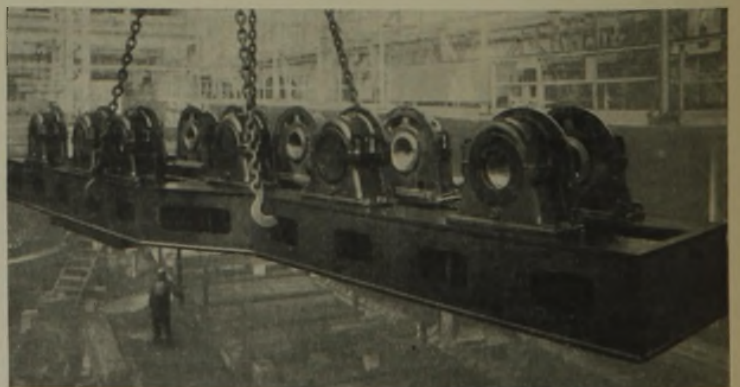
Geschweißtes Getriebegehäuse für kontinuierlichen Walzwerksantrieb.
